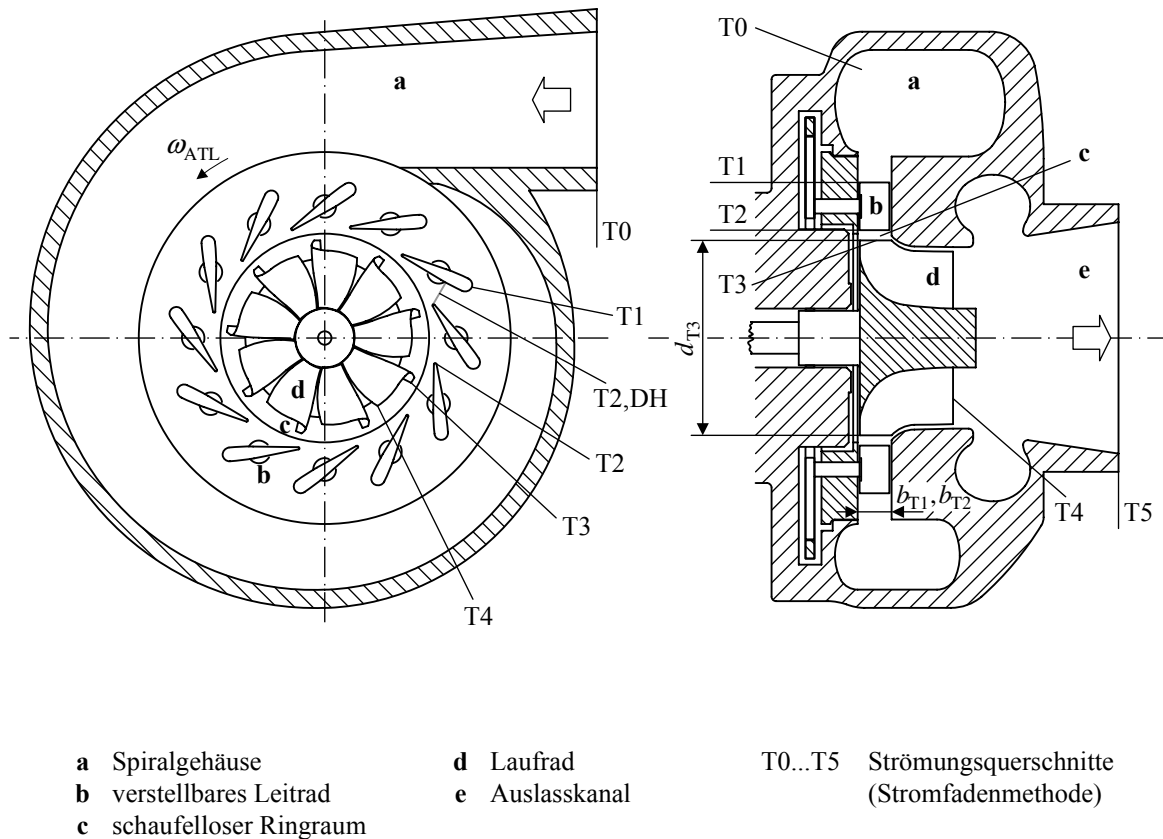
Schematischer Aufbau und Indizierung der Radialturbine mit verstellbarer Geometrie
